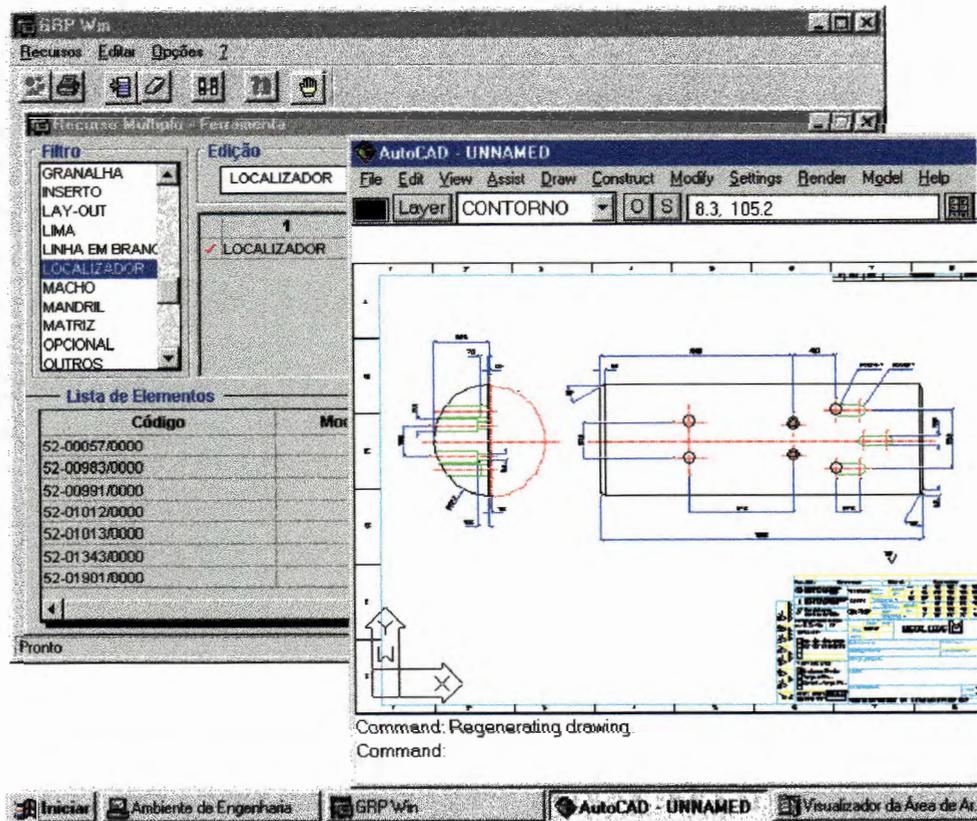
Desenho CAD executado automaticamente a partir do GRP
